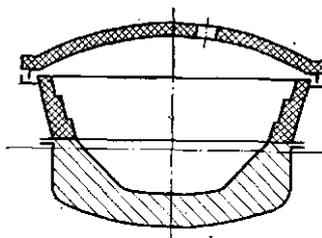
Цилиндро-конический кожух дуговой сталеплавильной печи
